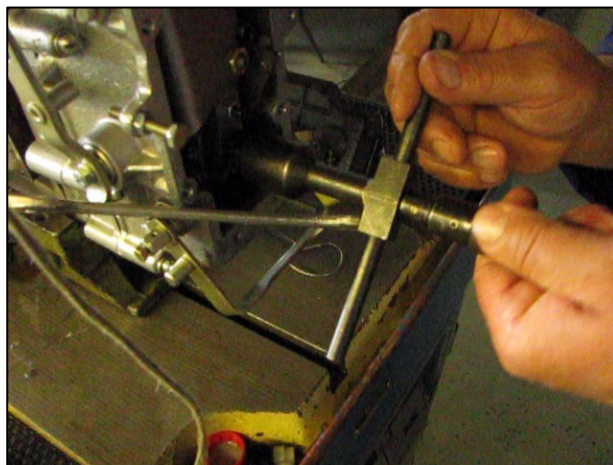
Вворачивание корпуса корректора в рычаг регулятора
